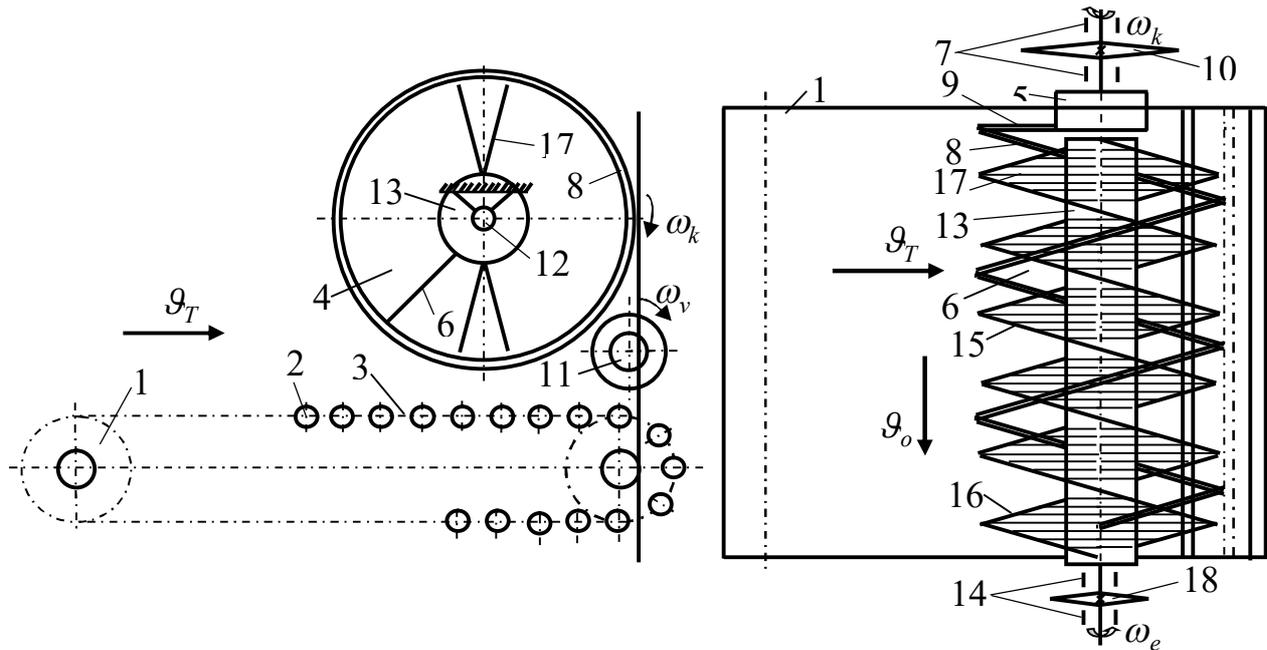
Конструктивна схема очисника вороху: 1 – подавальний транспортер; 2 – пруток; 3 – робоча гілка; 4 – комбінований робочий орган; 5 – пустотілий гвинтовий циліндр; 6 – виток; 7, 14 – опора; 8 – труба; 9 – фланець; 10, 18 – зірочка; 11 – відкидний валець; 12 – приводний вал; 13 – барабан; 15, 16 – гвинтова лінія; 17 – очисні елементи.
